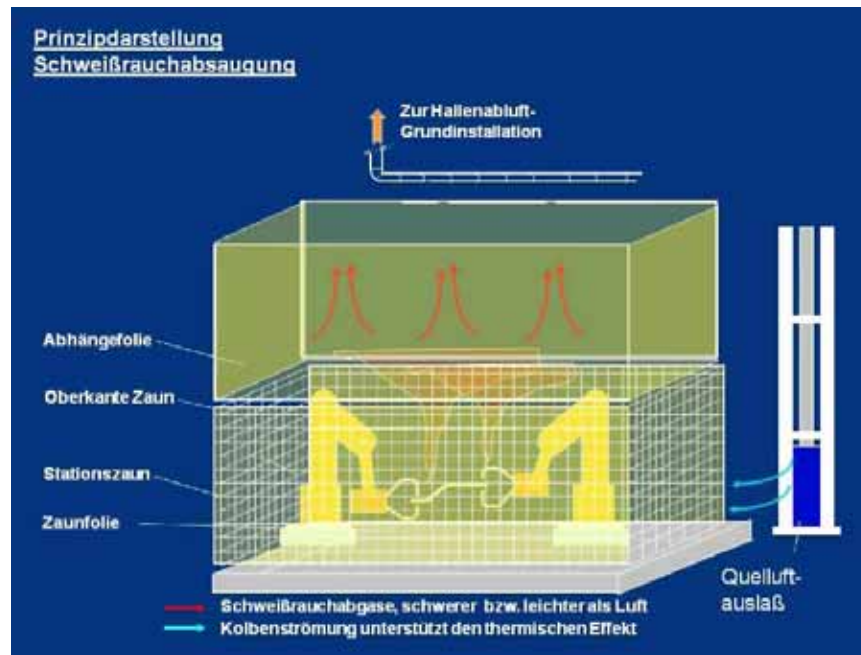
Technik der Schweißrauchabsaugung
